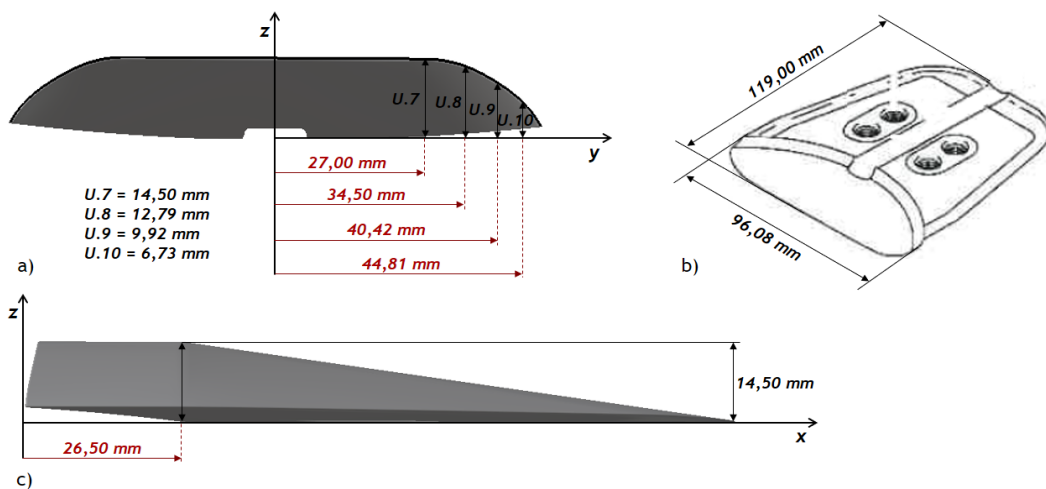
Dimensionamento do Scoop P25 (P/N:335-108-102-0): a) vista do perfil frontal do Scoop; b) vista isométrica com as principais dimensões nominais; c) vista lateral. Adaptado de [100].
